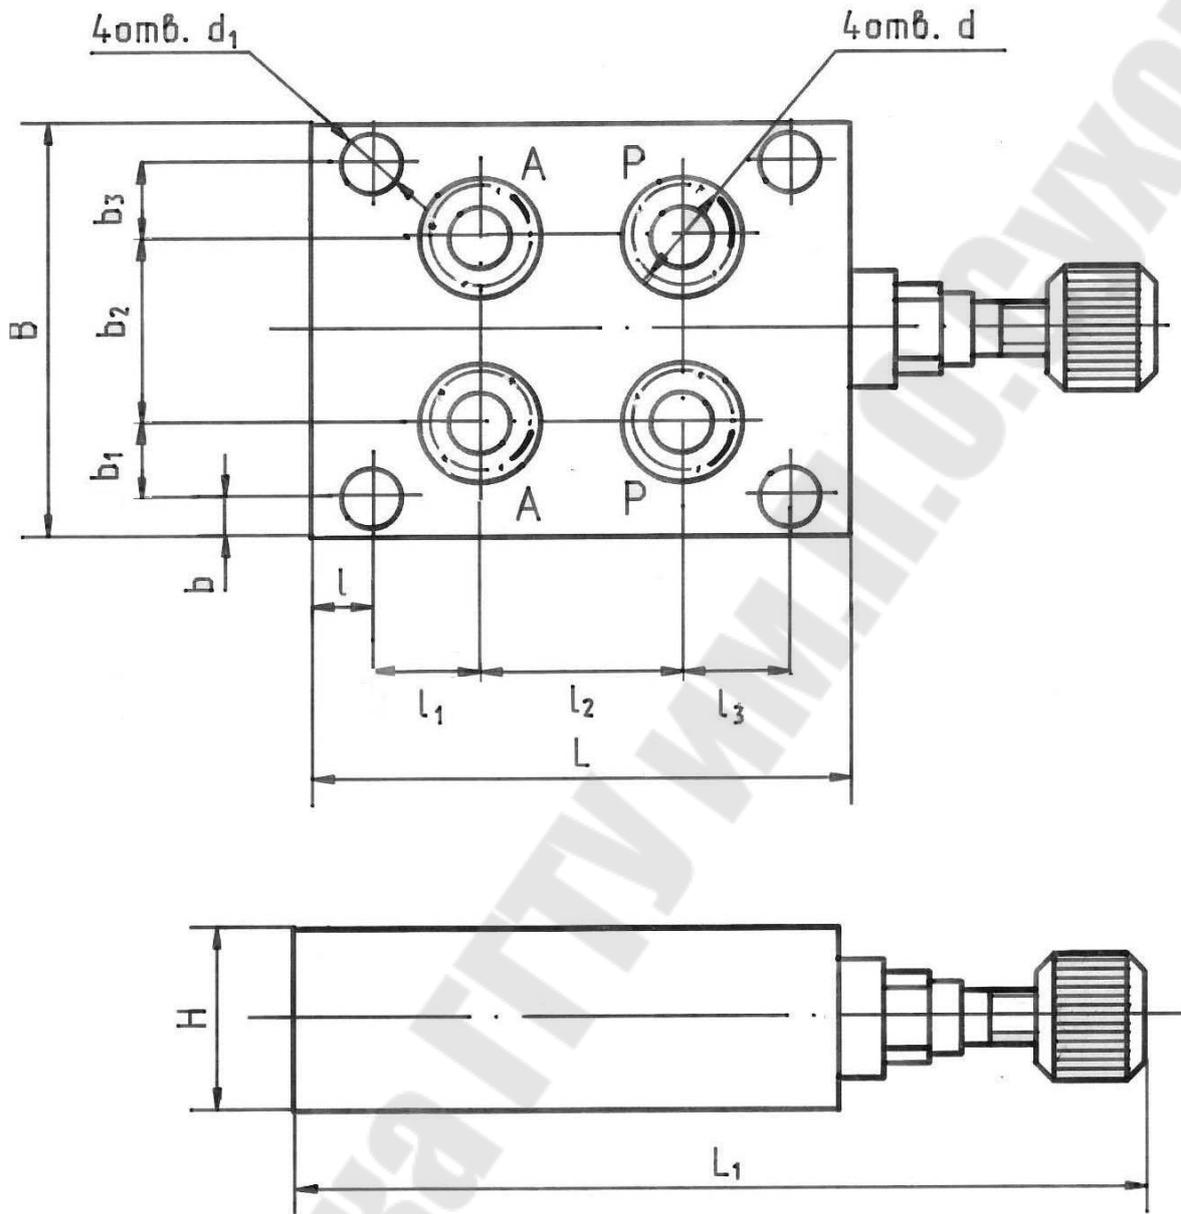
Общий вид блока присоединительного регулятора расхода
